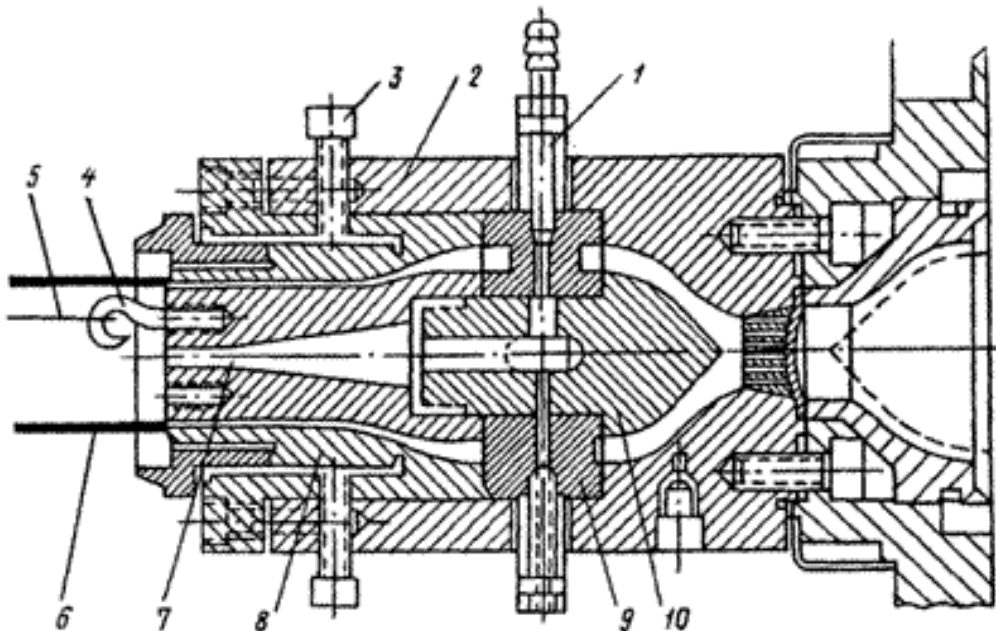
Прямотечійна кільцева головка для виготовлення труб і шлангів: 1 – штуцер для підведення стисненого повітря; 2 – корпус; 3 – регулювальні гвинти; 4 – кріпильний пристрій; 5 – трос для втримання ковзних пробок у трубі; 6 – трубна заготовка; 7 – канал для надходження в трубу стисненого повітря; 8 – матриця; 9 – дорнотримач; 10 – дорн
